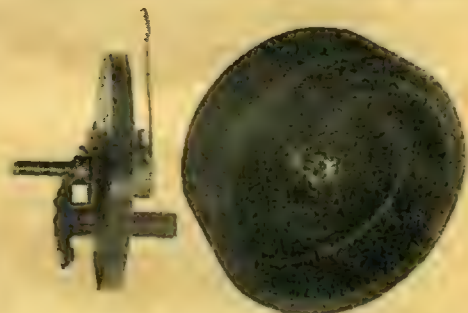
Ручка-верньер с четырьмя зубчатыми колесами. Направо видна ручка-крышка внутри которой видна маленькая зубчатка.
